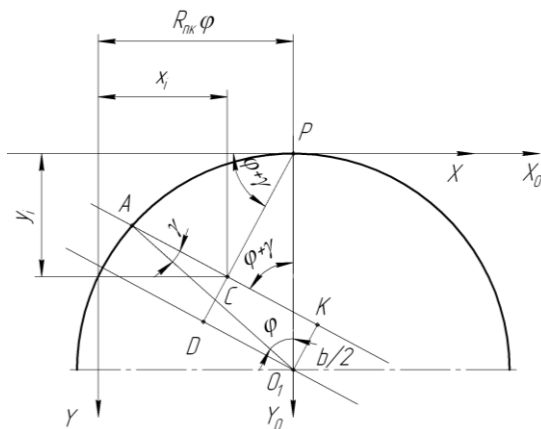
Аналітичне профілювання фрези для обробки шліцевого вала
